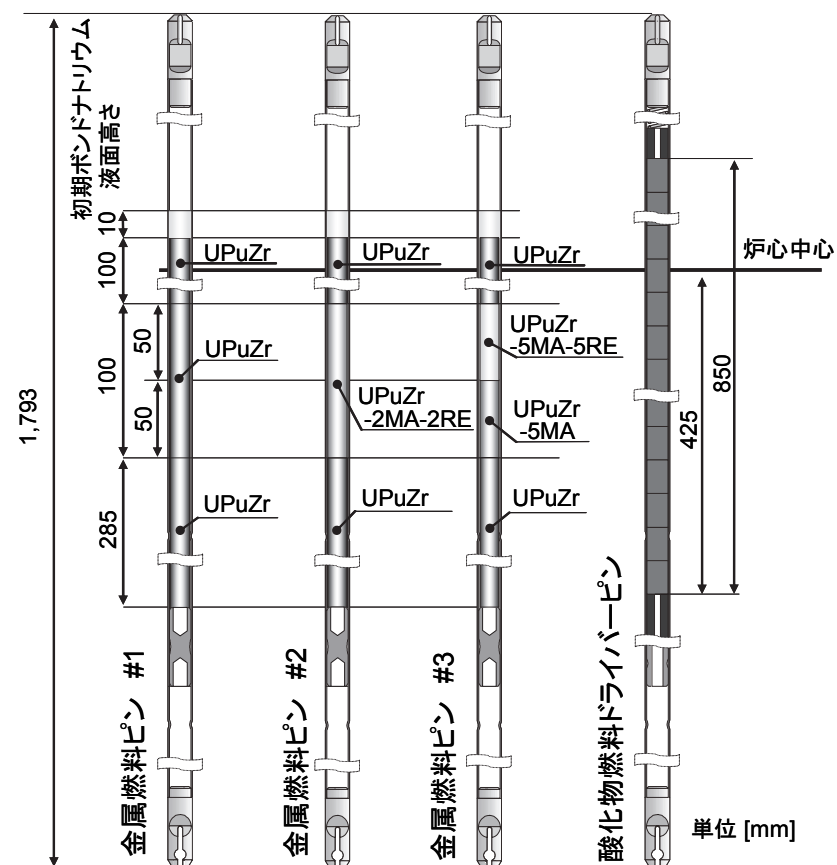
MA 含有金属燃料ピンの軸方向配置図 [2.2-6]
